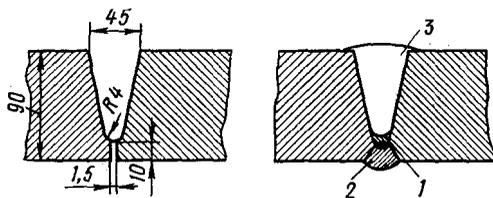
Форма разделки кольцевого стыка под многослойную сварку
